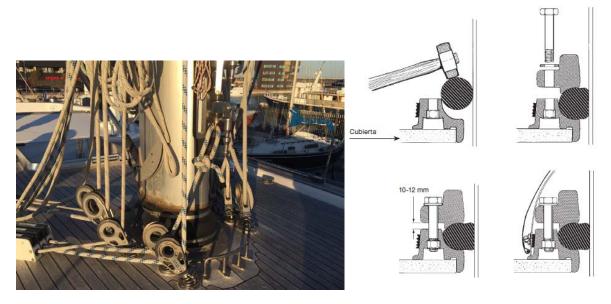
Fogonadura y sección de fogonadura en dos partes. Fuente: Propia / Seldén
